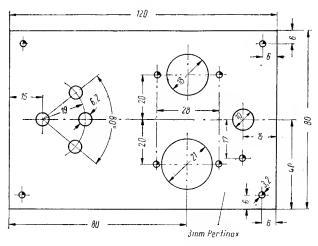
Maßskizze für die Frontplatte des Durchgangsprüfers
